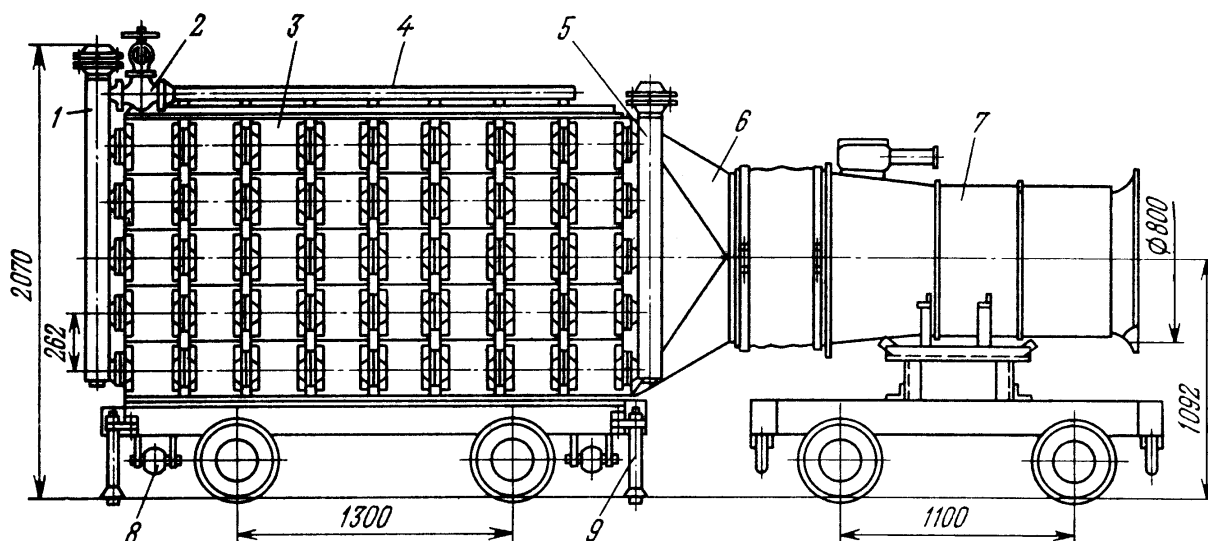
Шахтный агрегатированный воздухоохладитель типа АРВЭ: 1, 5 – коллекторы для подвода и отвода хладоносителя соответственно; 2 – вентиль для подачи промывочной воды; 3 – секция; 4 – промывочный коллектор; 6 – диффузор; 7 – вентилятор; 8 – каток; 9 – домкрат
